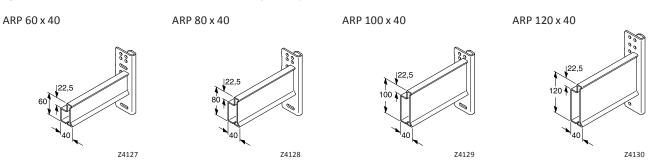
Sections transversales des traverses ARP (dimensions toujours indiquées en mm, connecteur soudé au milieu)
